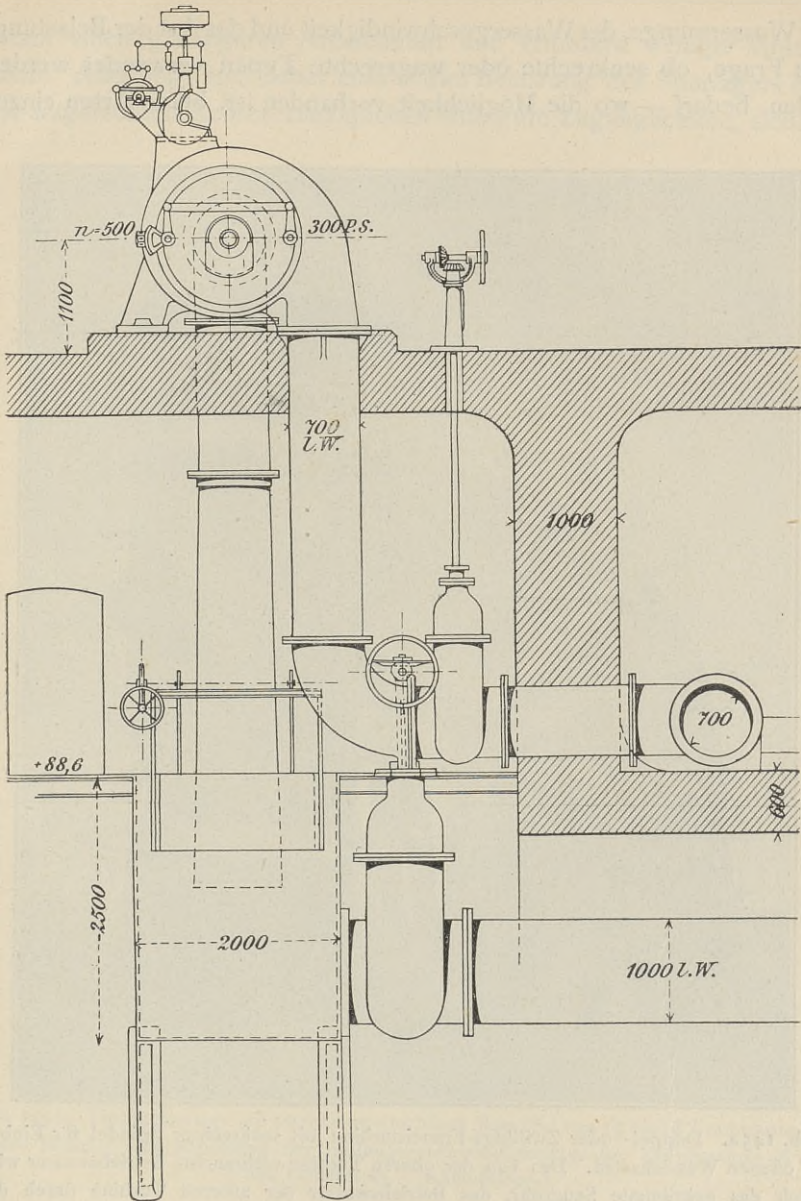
Francisspiralturbine auf wagerechter Welle mit gußeisernem Gehäuse für Dynamobetrieb.
